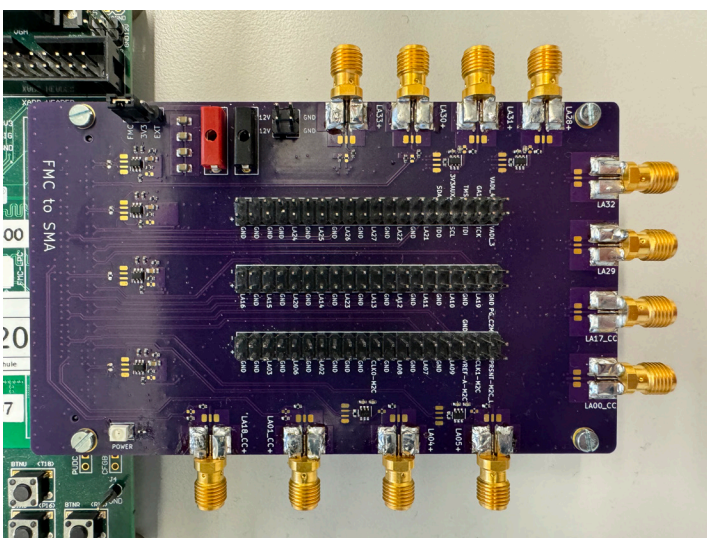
Fertig produziertes PCB im Einsatz auf einem ZedBoard
